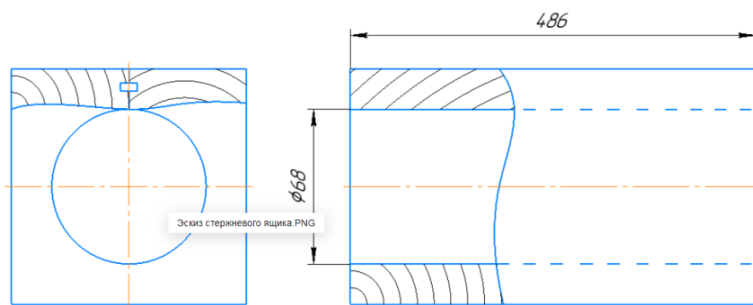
Стержневой ящик для изготовления детали «втулка»
